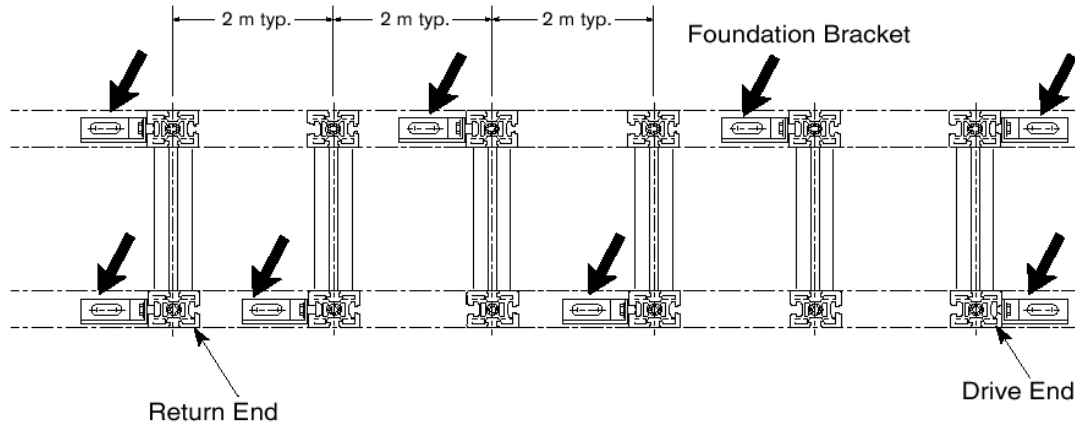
Esquema de ensamblaje de estructura prefabricada [16]
